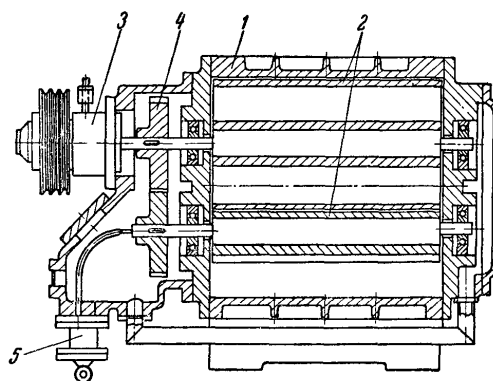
Схема устройства двухроторного насоса. 1 — корпус; 2 — роторы; 3 — привод; 4 — шестерни связи; 5 — маслонасос.
